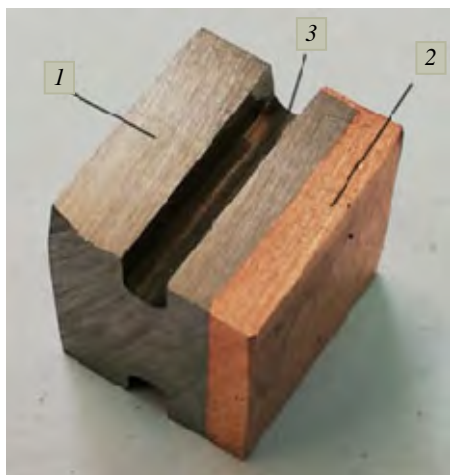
Макет вольфрамового модуля облицовки дивертора: 1 — вольфрам; 2 — медь; 3 — проточка для крепления в камере установки ПЛМ
